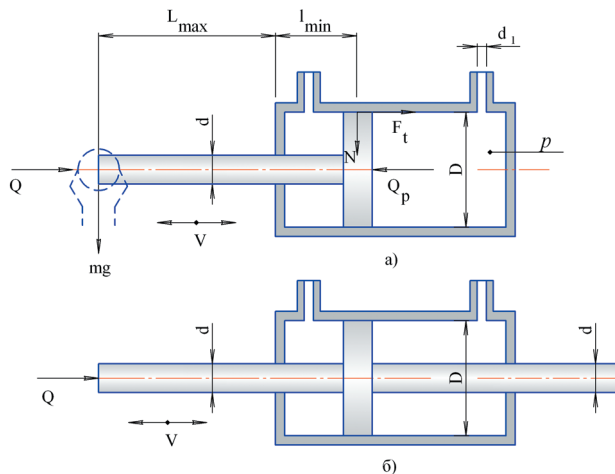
Розрахункова схема поршевого пневматичного приводу
